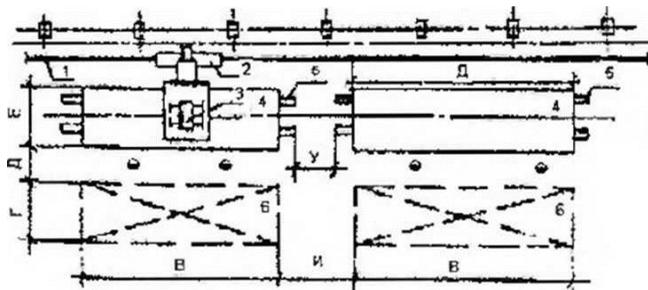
Размещение установки велосипедной тележки для автоматической сварки продольных и кольцевых швов цилиндрических изделий: I - направляющий рельс;
